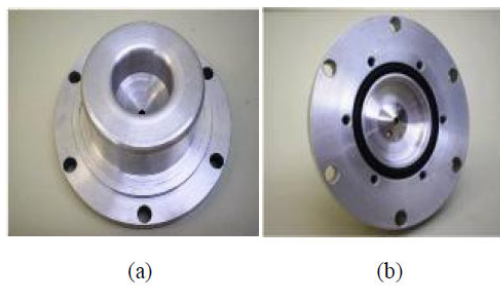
Cone metálico conectado acima da plataforma superior na estrutura interna da fonte termiônica (primeiro eletrodo do sistema de extração)
